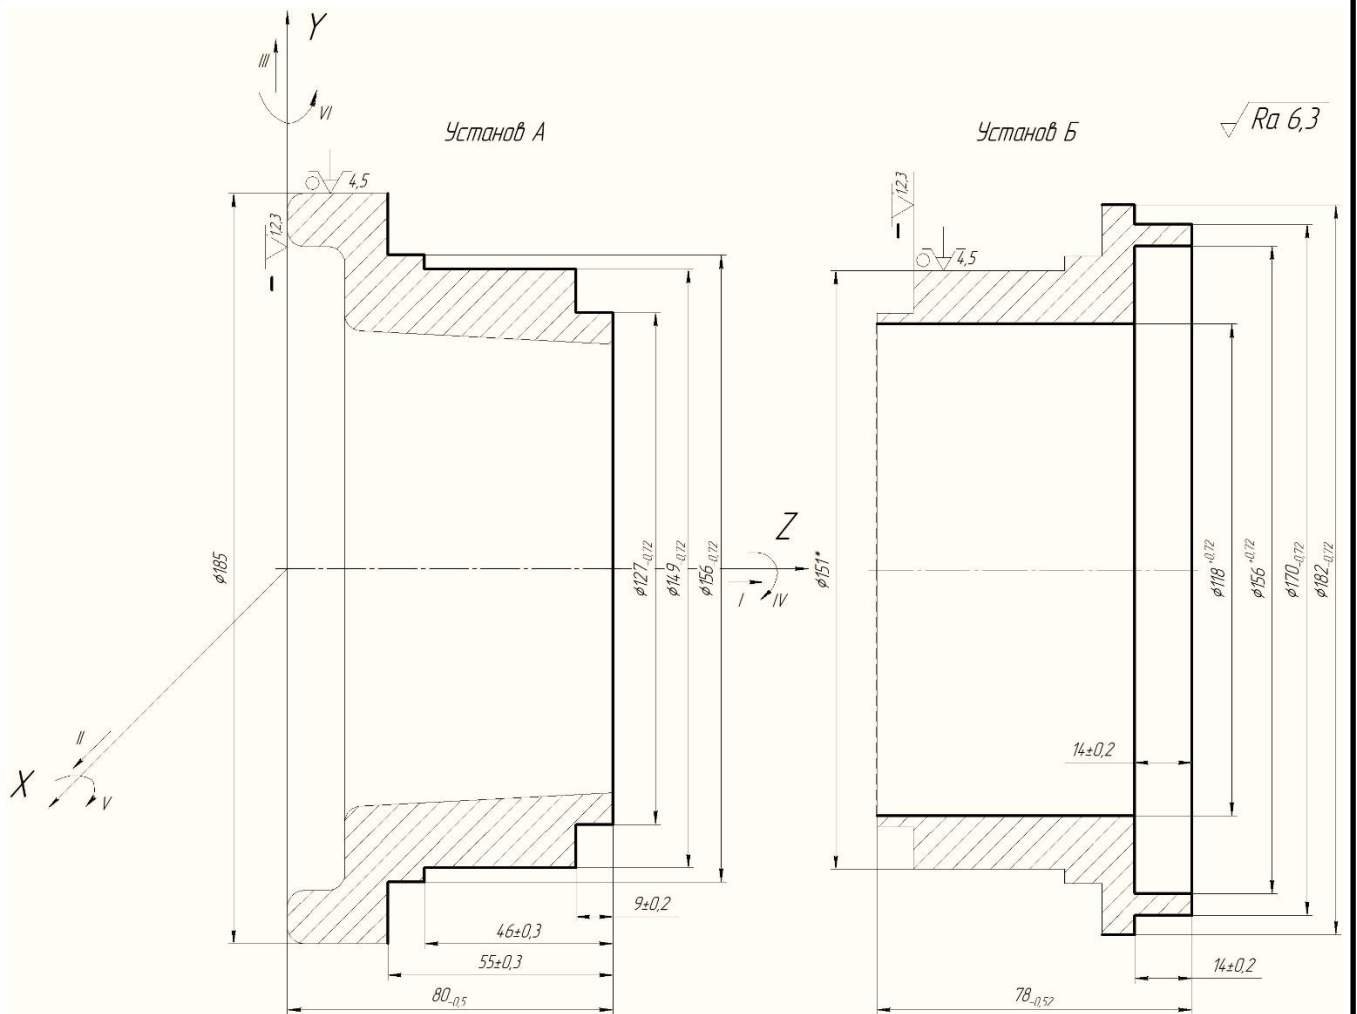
Схема установки заготовки на токарній операції (варіант 1)
